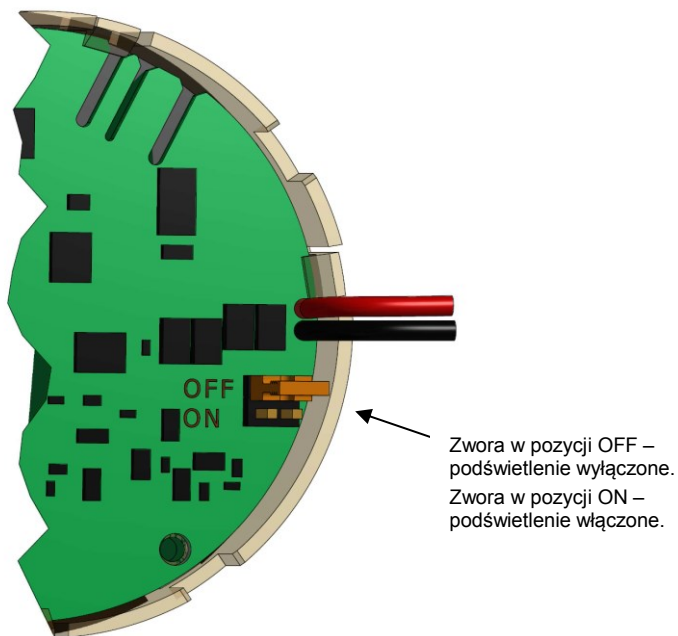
Widok przetwornika po zdemontowaniu pokrywy wyświetlacza
